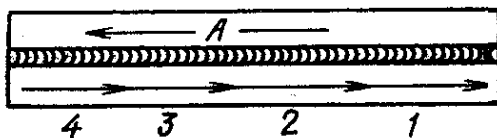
Сварка швов средней длины обратноступенчатым способом
